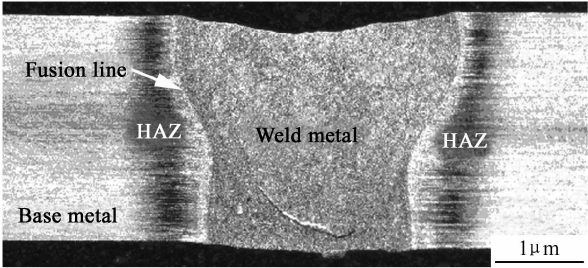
5A90 铝锂合金激光焊接头横截面形貌
